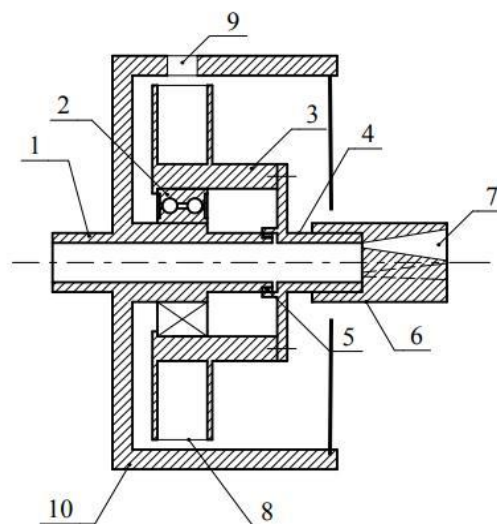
Пристрій для створення обертового гідравлічного струменя
